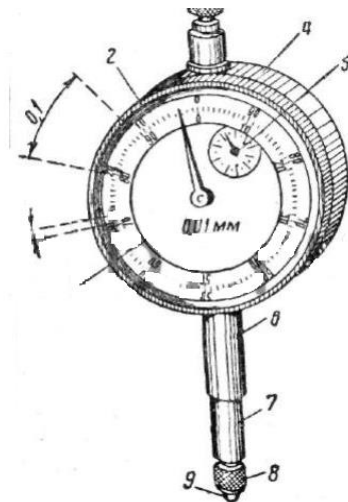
Индикатор: а) общий вид часового индикатора: 1-циферблат, 2-обод, 3-голдовка, 4-корпус, 5-циферблат, 6-втулка, 7-измерительный стержень (шпиндель), 8-наконечник, 9-шарик.
